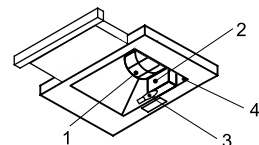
а. Kamilla 600, Kamilla 500, Kamilla 450
